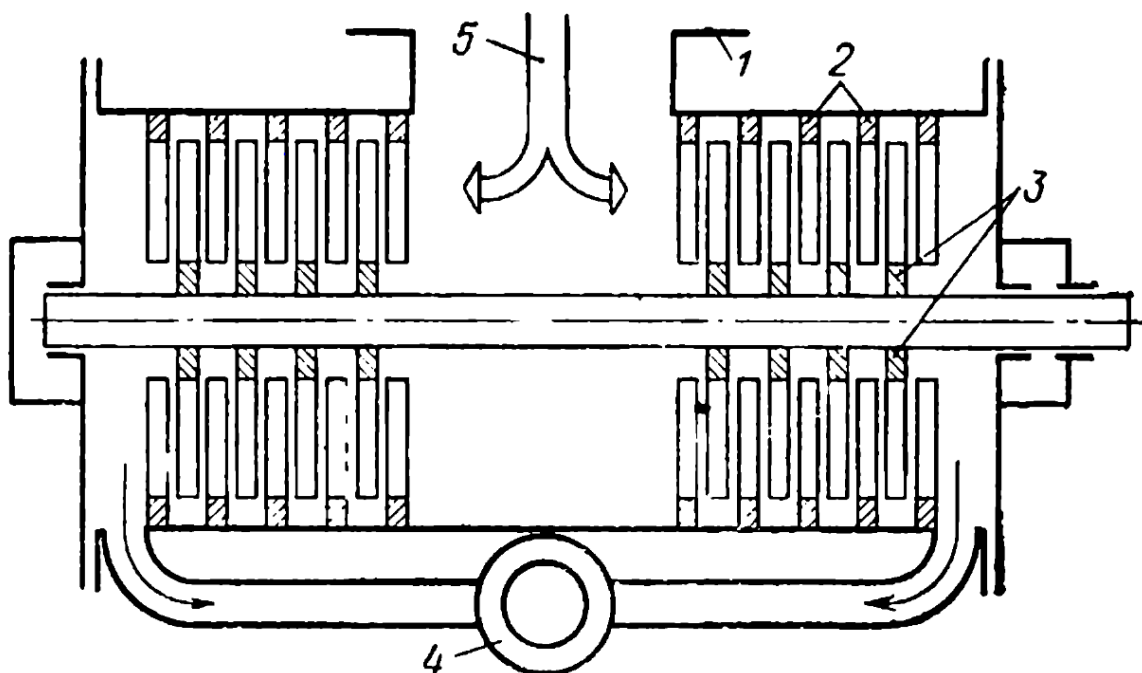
Схема турбомолекулярного насоса. 1 – корпус; 2 – статорные диски; 3 – роторные диски; 4 – выпускной патрубок; 5 – впускной патрубок [5, с. 130]
